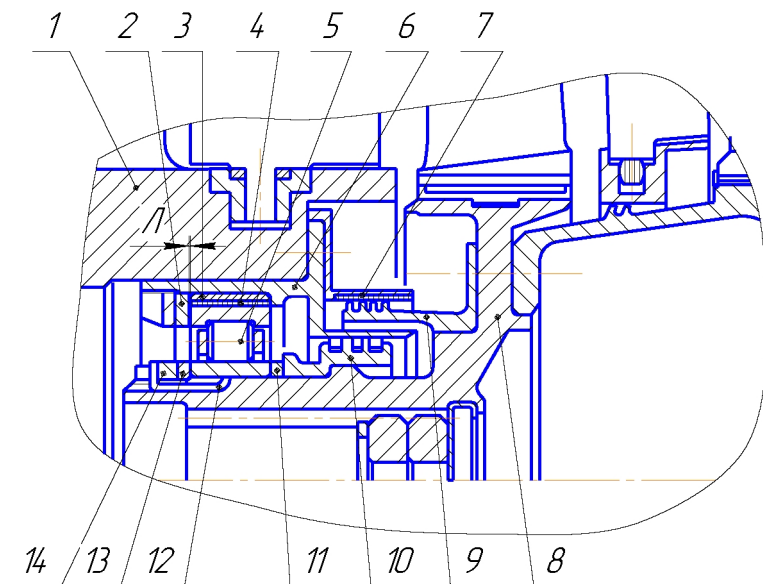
Передняя опора компрессора 1-орпус опоры;
